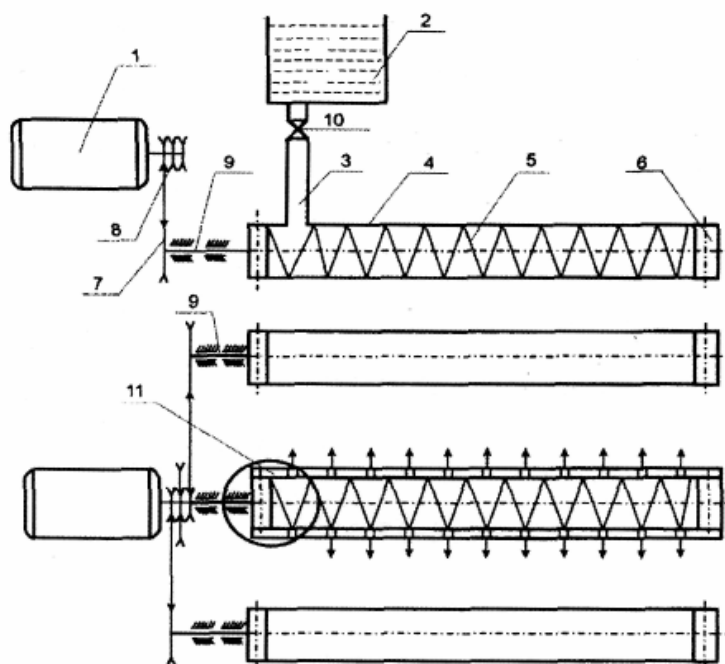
Привод 3-х пружин одним двигателем:
